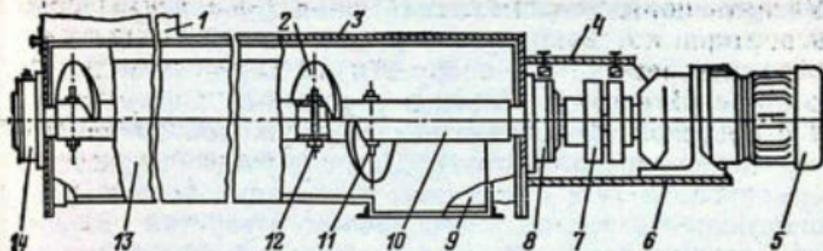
Загрузочный транспортер КПГ-10.46.06:
